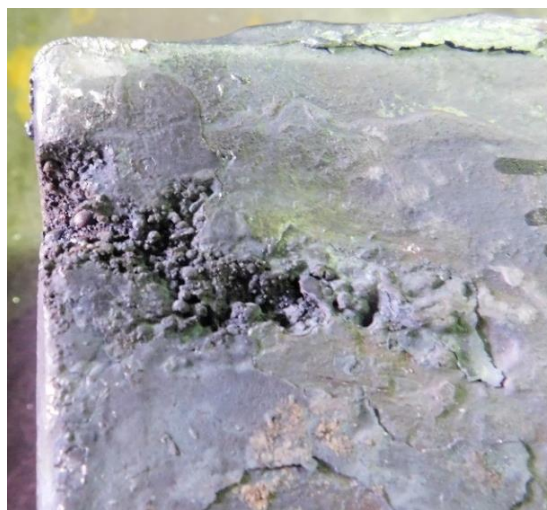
Поверхня заготовки з дефектом сталь СтЗсп
